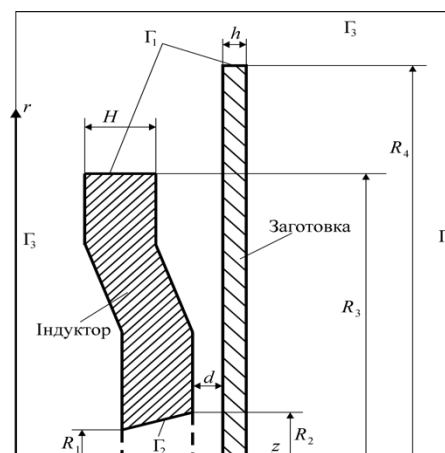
Розрахункова схема розрахункова схема складеного одновиткового індуктора та плоскої заготовки
